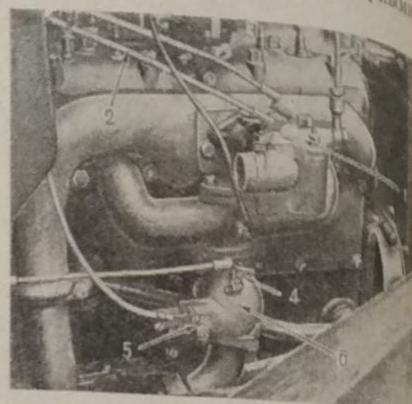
Смеситель газа и карбюратор двигателя ГАЗ с установкой Г-21
